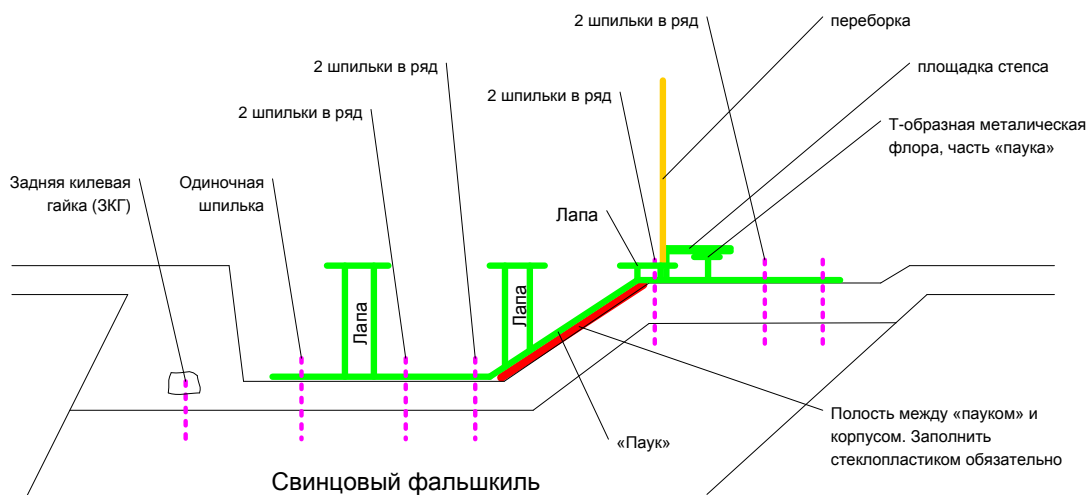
Продольный разрез системы подвеса фальшкиля.
